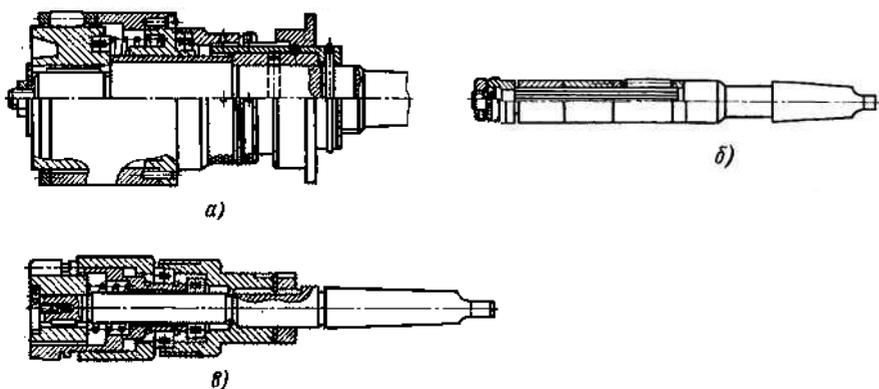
Багатороликові розкатки для обробки: а, б — навскрізних циліндричних отворів; в — глухих циліндричних отворів
